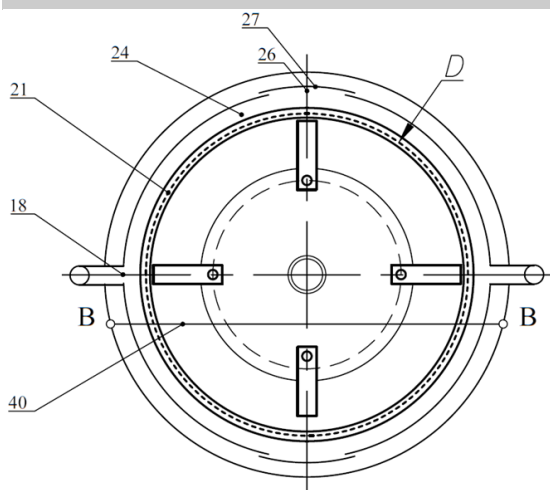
Разрез дробилки-смесителя по Б-Б (рис. 2)
